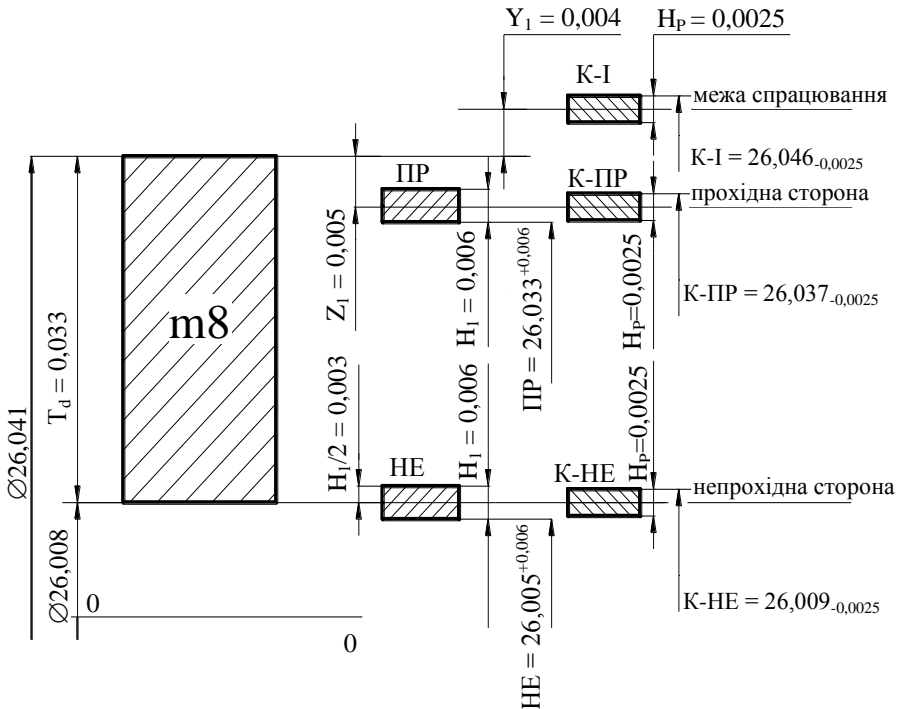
Схема розміщення полів допусків калібр - скоби Ø26 m8
